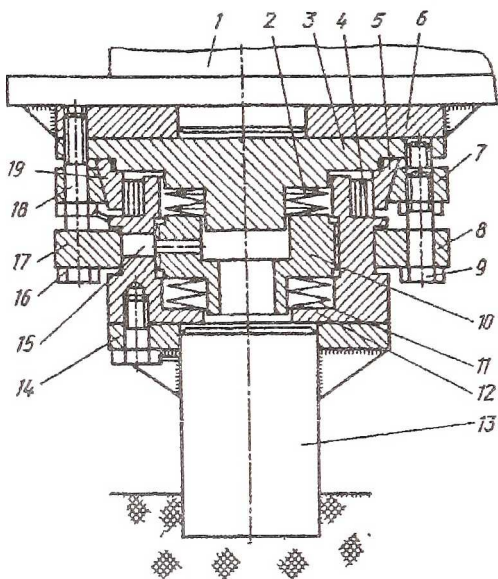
Упругодемпферная подвеска основания мельницы для размола какао-бобов РС-1000: 1 -основание; 2, 11 - набор тарельчатых пружин (пакет шайб Бельвиля); 3, 10, 12 промежуточные направляющие; 4 радиальный пакет гофрированных кольцевых пластин; 5, 19 - набор конических секторов; 6, 14 - промежуточные основания; 7 - зажимная конусная обойма; 8, 17 технологические полукольца; 9, 16, 18 - крепежные элементы; 13-опора; 15 - технологическое отверстие (паз)
